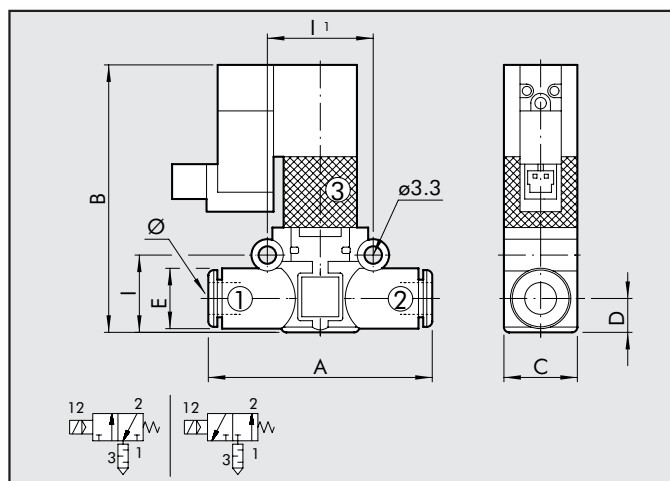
Abb. C: Wandbefestigung der SOV L mittels zweier Schrauben
